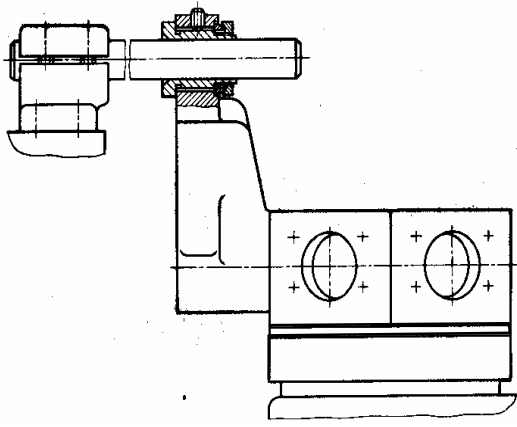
Схема центрування револьверної головки за допомогою напрямної штанги
